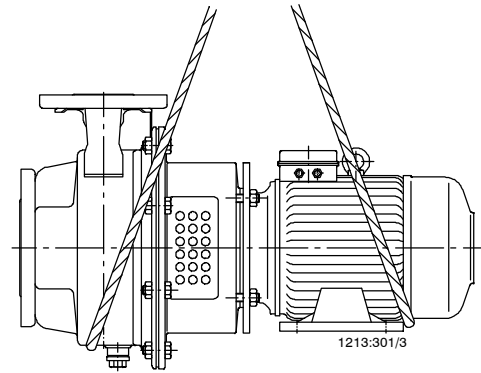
Транспортировка насосного агрегата с опорной лапой двигателя
